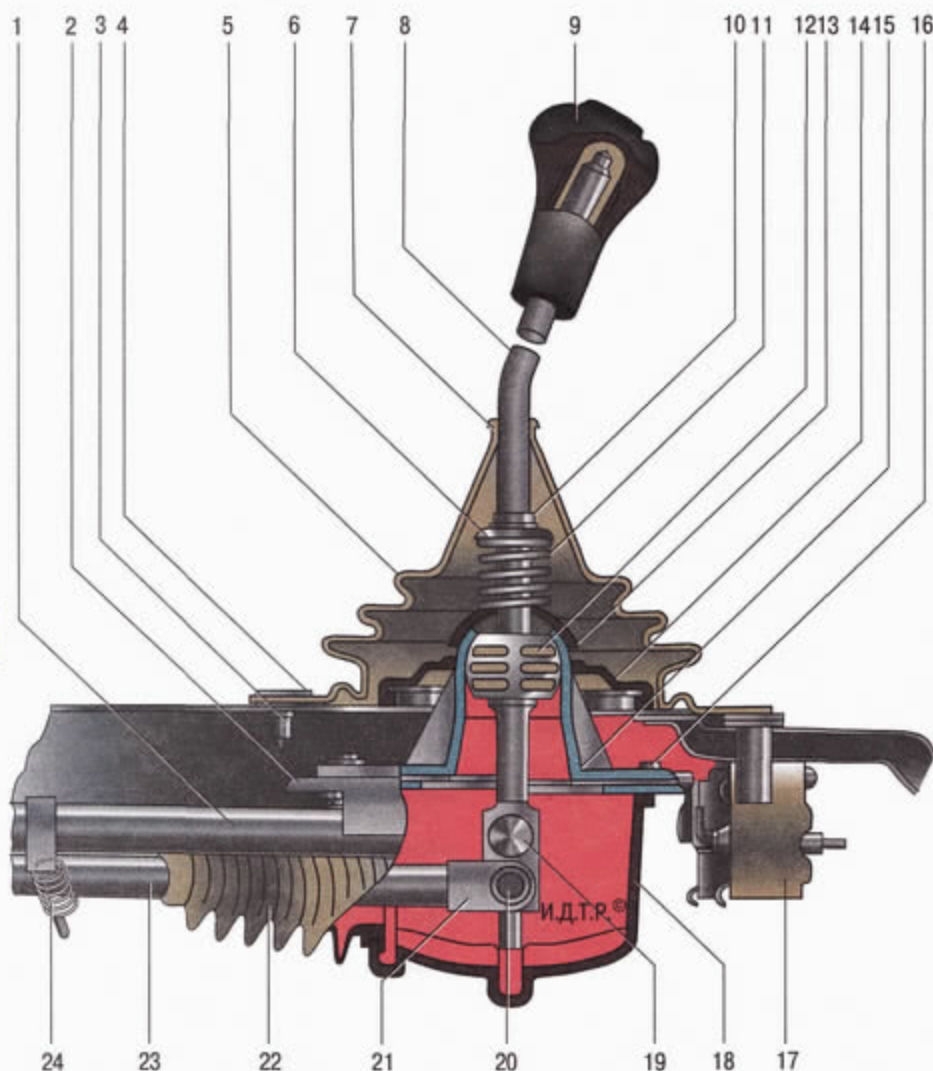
Привод управления коробкой передач: 1 – реактивная штанга; 2 – основание привода; 3 – втулка поршня; 4 – поршень; 5 – чехол; 6 – упорная шайба; 7 – фиксатор чехла; 8 – рычаг управления; 9 – рукоятка; 10 – стопорная шайба; 11 – пружина рычага; 12 – сферическая головка; 13 – чашка; 14 – уплотнитель; 15 – опора; 16 – гайка крепления с опорой; 17 – резиновая муфта; 18 – крышка; 19 – подвижный упор; 20 – неподвижный упор; 21, 23 – валы управления; 22 – чехол; 24 – пружина
